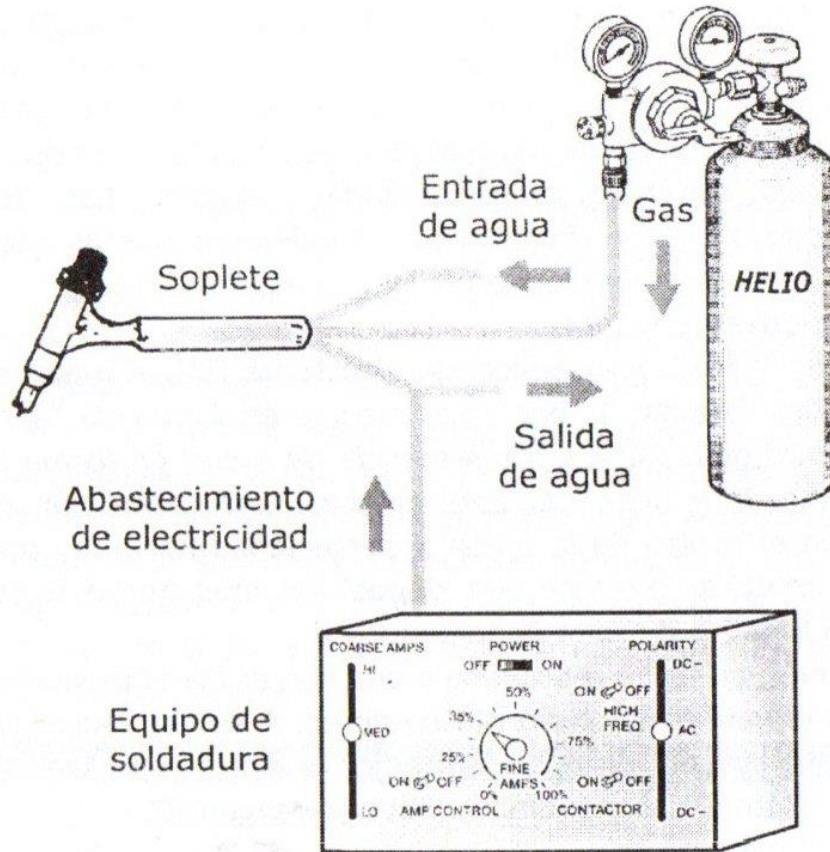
Esquema de un sistema para soldadura de arco TIG
